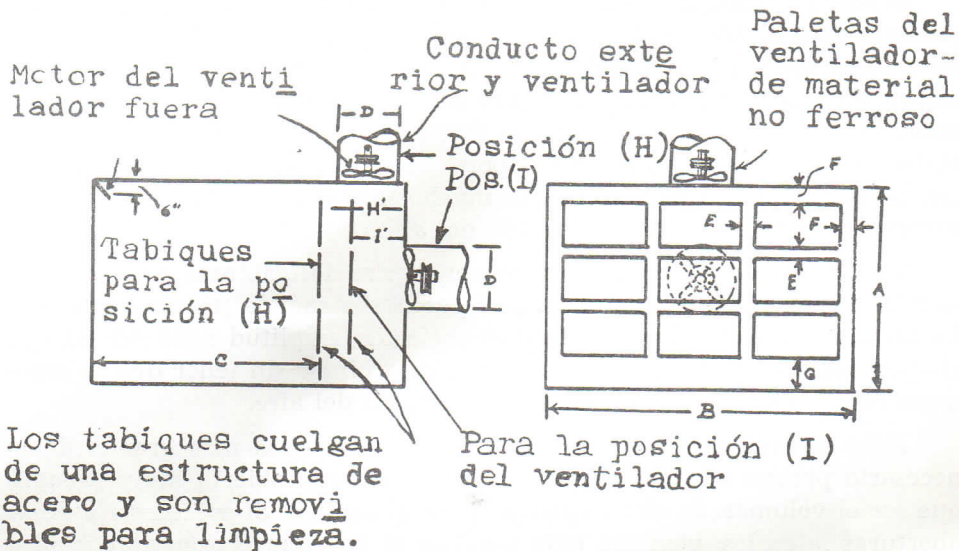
GABINETE PARA PINTURA A PISTOLA
